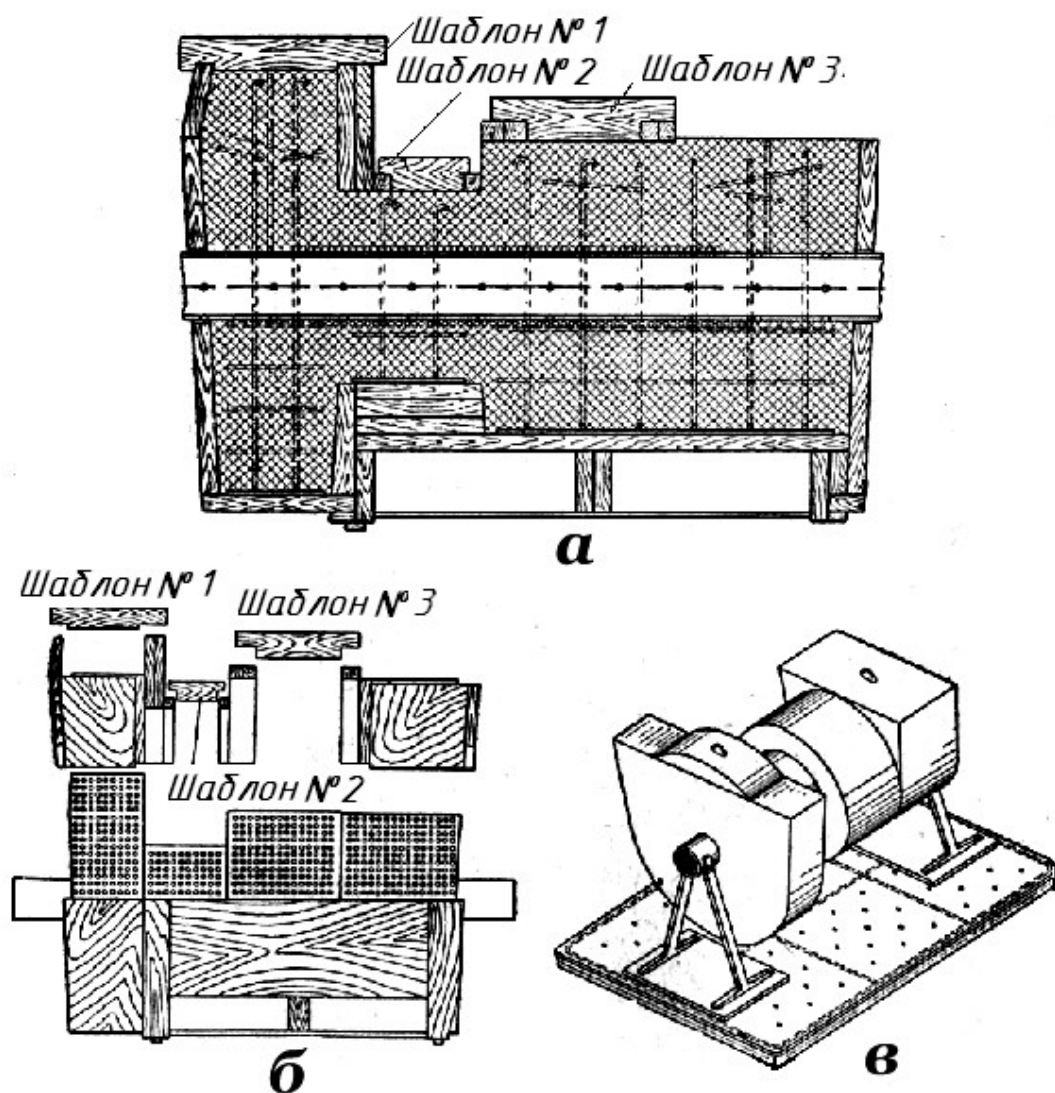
Изготовление стержня для станины прокатного стана: а – расположение шаблонов, каркасов и патрона; б – удаление отъемных частей; в – готовый стержень.
